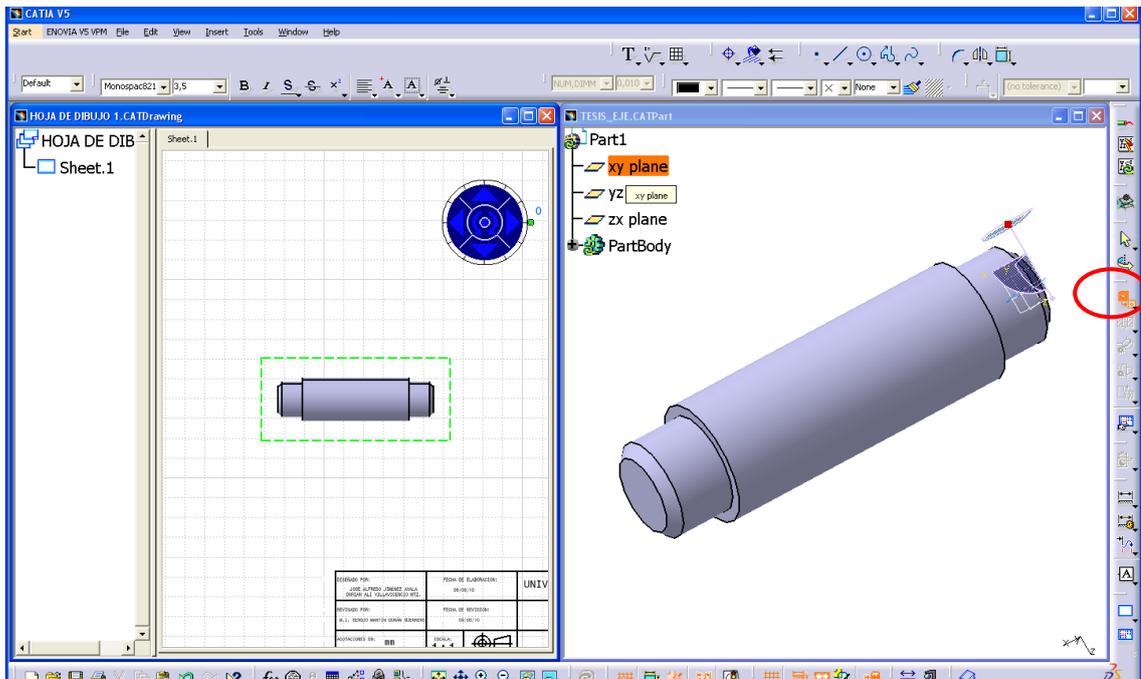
Icono front view y la vista frontal del dibujo en la ventana de drafting.
